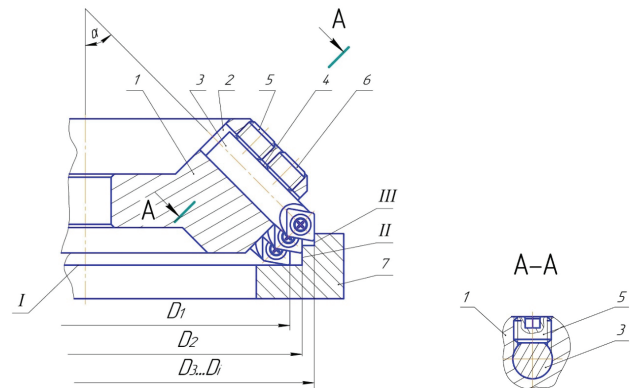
Осьовий переріз наструюваної торцевої фрези та наструювального калібру-кільця
